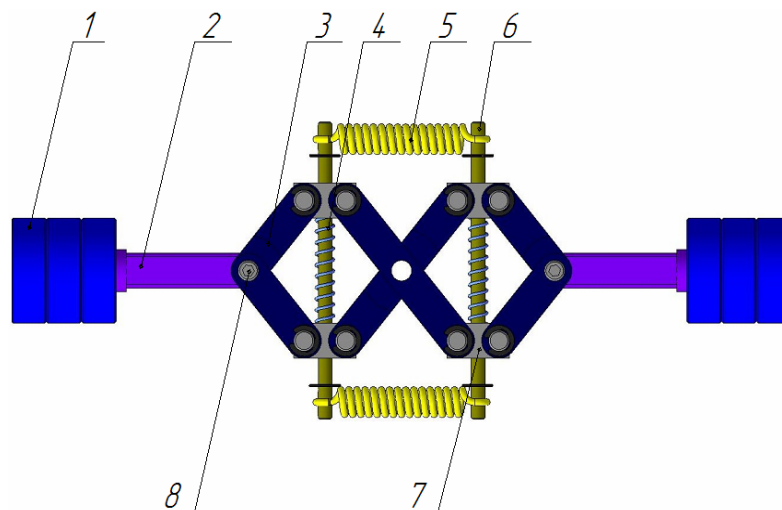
Рычажно-пружинный механизм устройства для алмазного выглаживания отверстий
